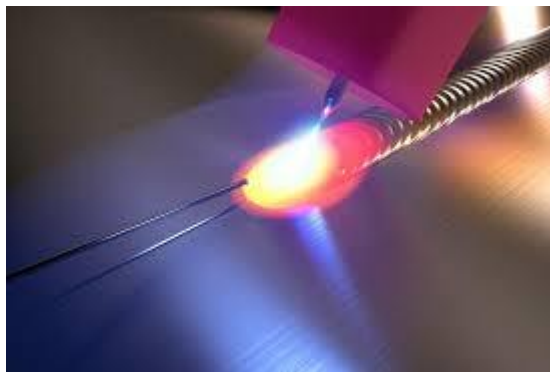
Proceso GTAW-TIG (Prosoldes, 2024)
